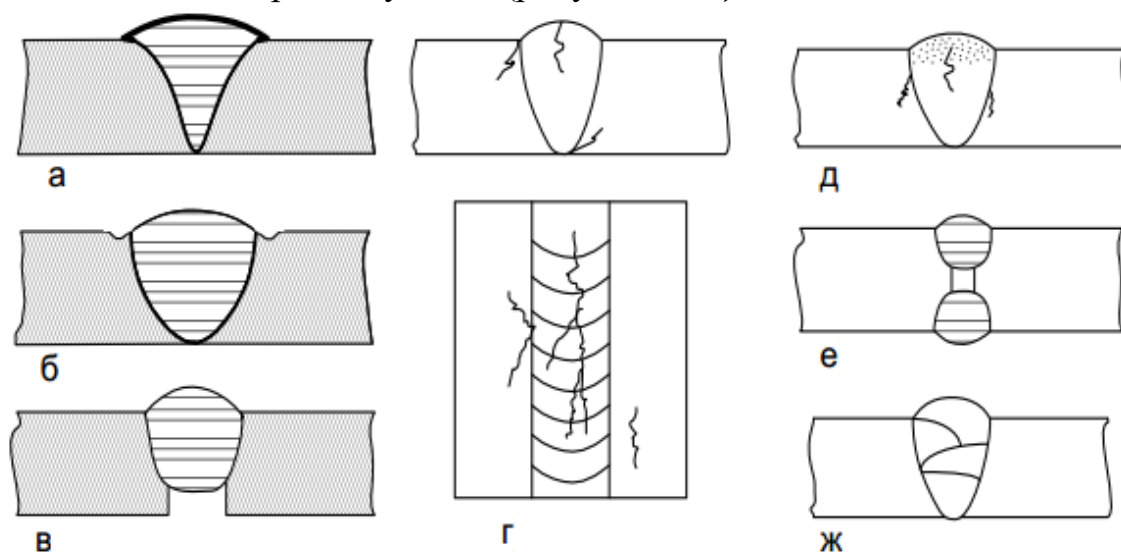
Види дефектів зварних з'єднань: а - наплив; б - підріз; в - непровар; г - зовнішні тріщини, пори; д - внутрішні тріщини і пори; е - внутрішній непровар; ж - шлакові відкладення
